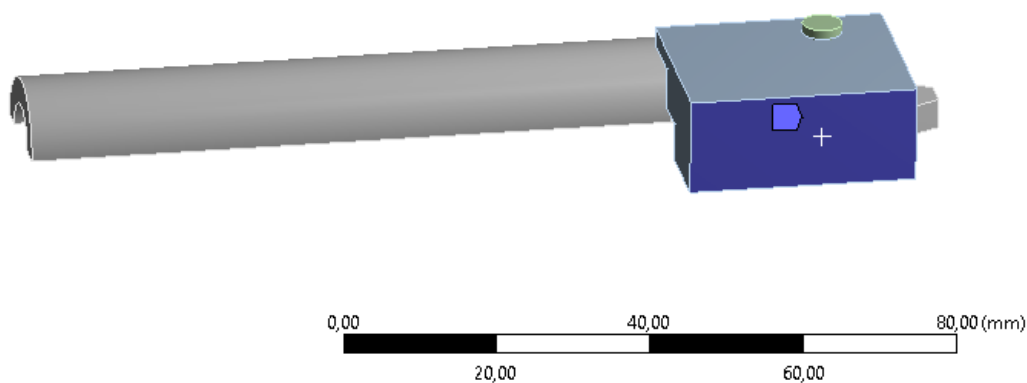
Okrajová podmínka Displacement na komponentu hlavně.
